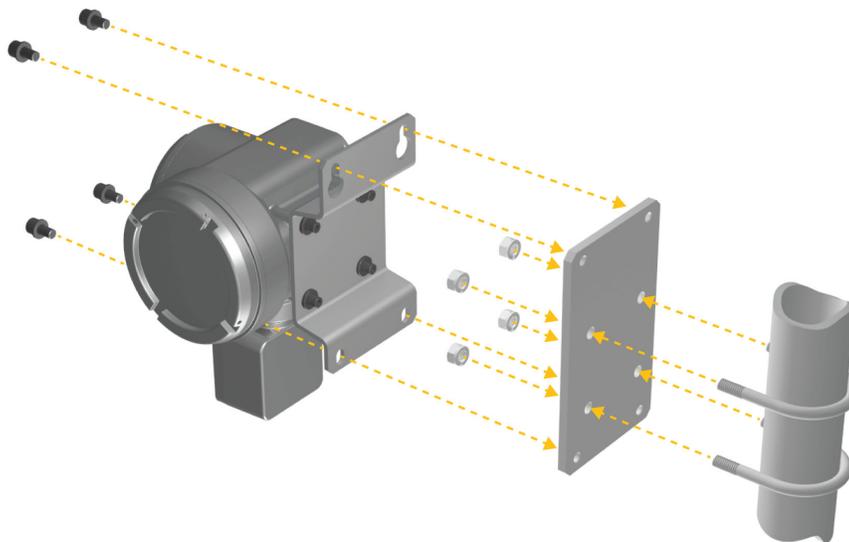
Крепление монтажного кронштейна на стойке для преобразователя в корпусе из нержавеющей стали
